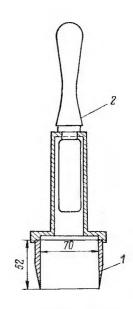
Приспособление для вырезания образцов режущим кольцом. 1— режущее кольцо; 2— ручка с упором.
